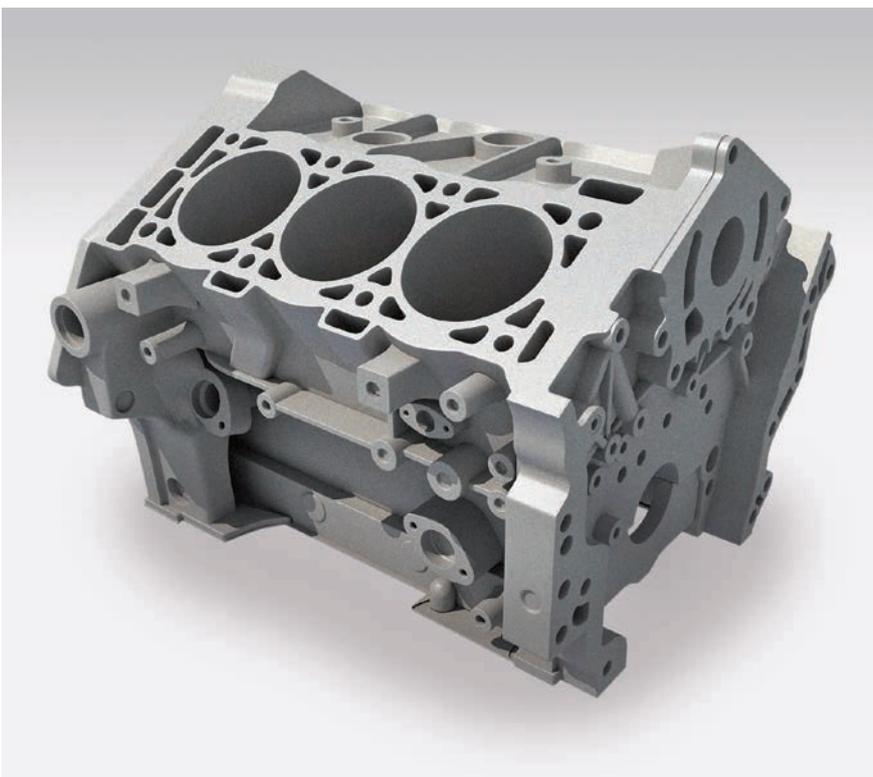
Алюминиевый блок цилиндров, изготовленный по аддитивной технологии
